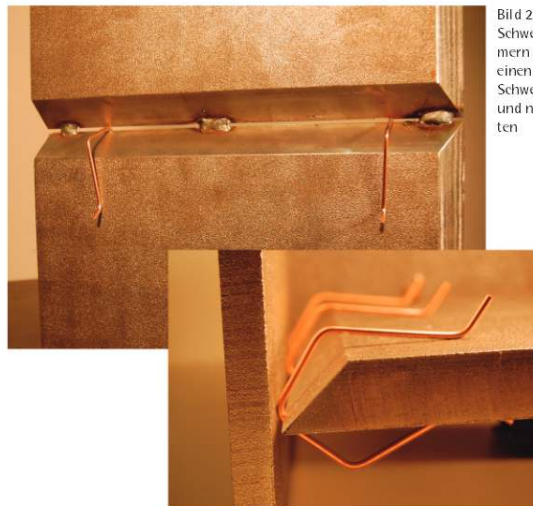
• Die Schweißspaltklammer sorgt für einen definierten Wurzelspalt – vor und nach dem Heften
